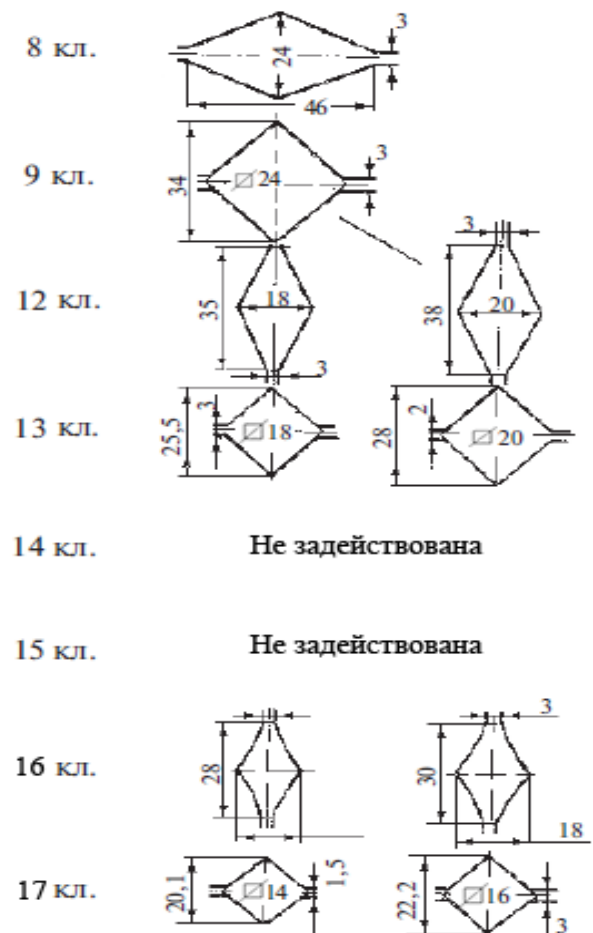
Калибровка промежуточной и чистовой групп клетей мелкосортного непрерывного стана 250-5 для прокатки квадратных профилей
